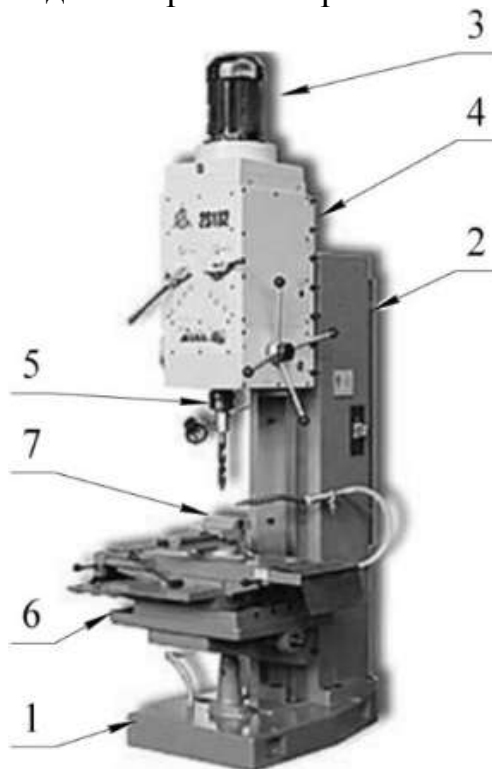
Загальний вигляд вертикально-свердлильного верстата моделі 2A135
